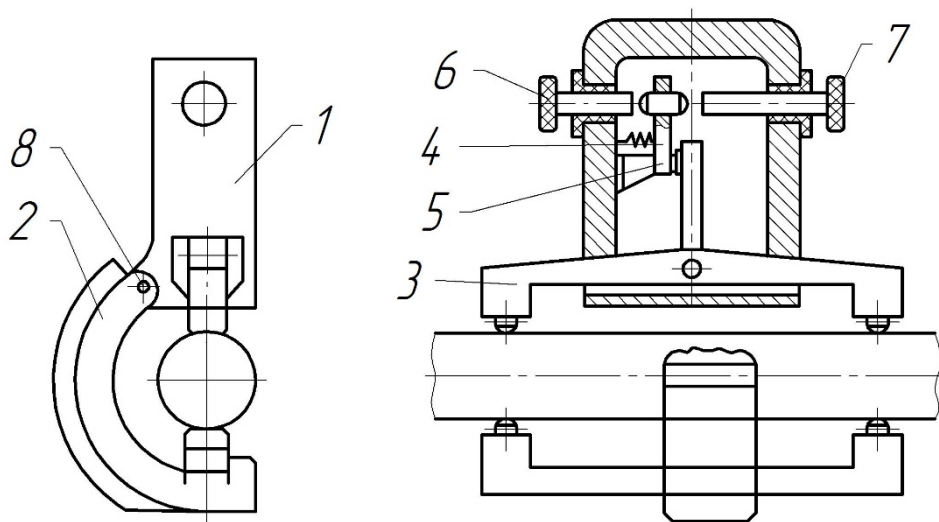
Прилад для вимірювання конусності циліндричної поверхні
